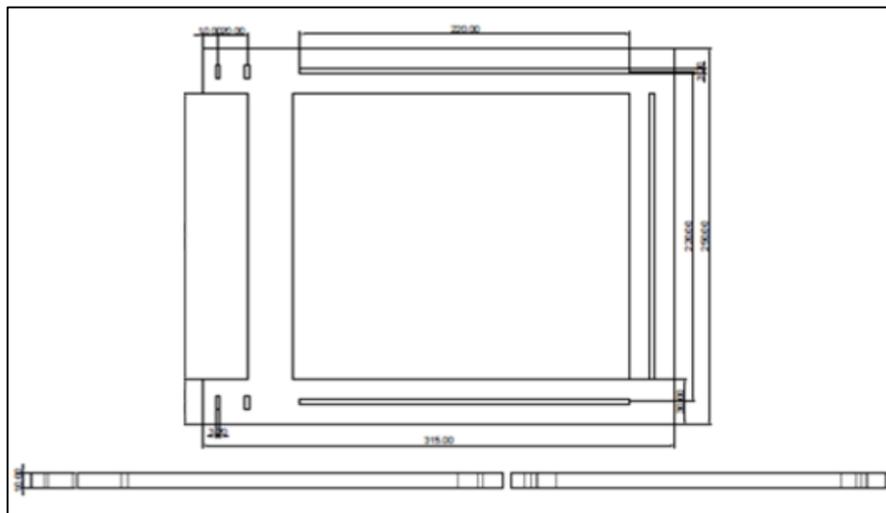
Desenho em CAD da tampa da base com a dobradiça.
